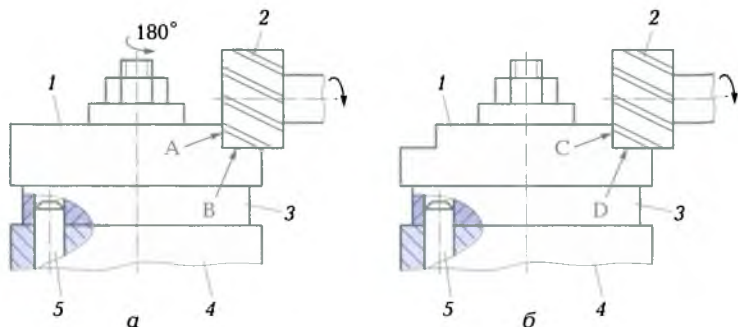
Схемы обработки заготовки в двух позициях (а, б):
